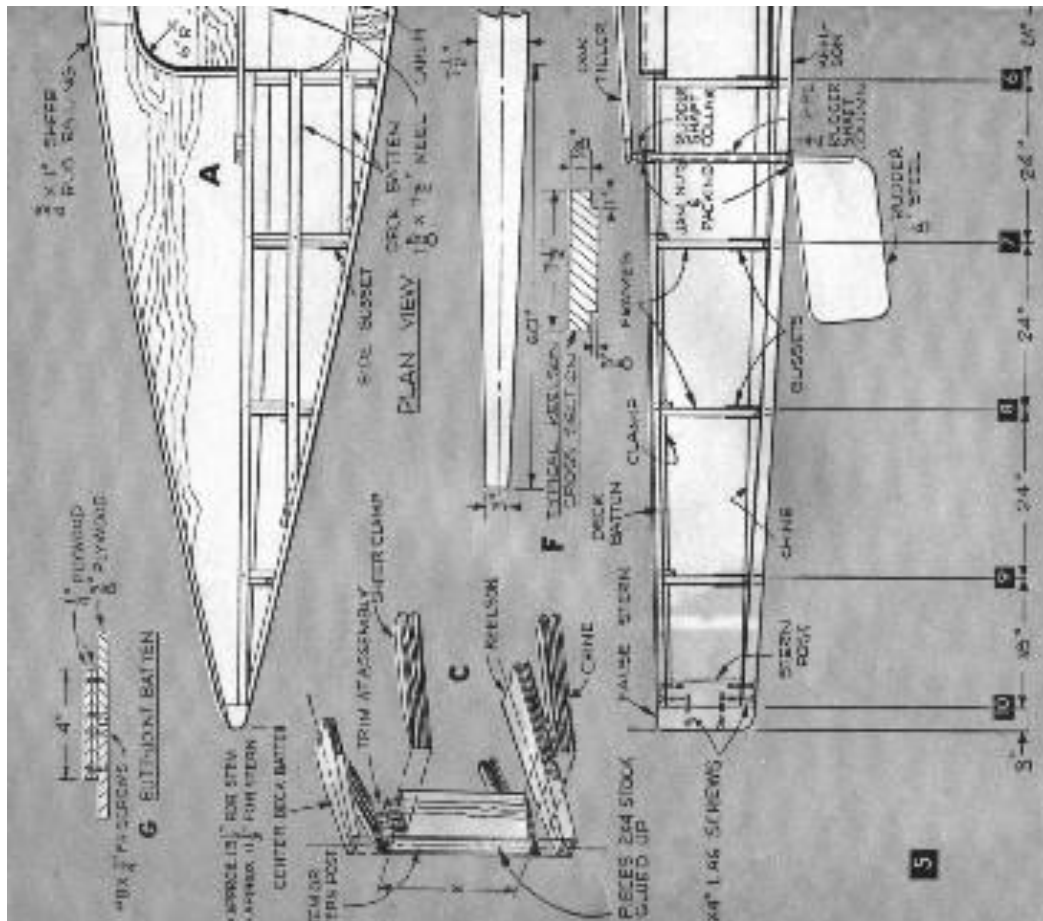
Planos planta y perfil estructura Missile (Fuente: Svensons.com)
